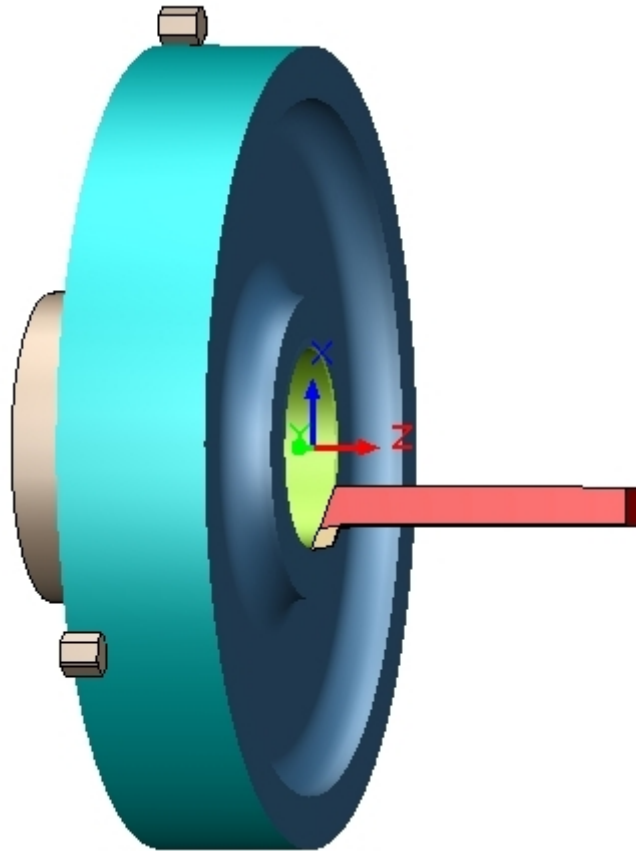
Фрагмент імітації обробки поверхонь 1, 2, 3, 12 – чистове розточування отвору розточувальним різцем
